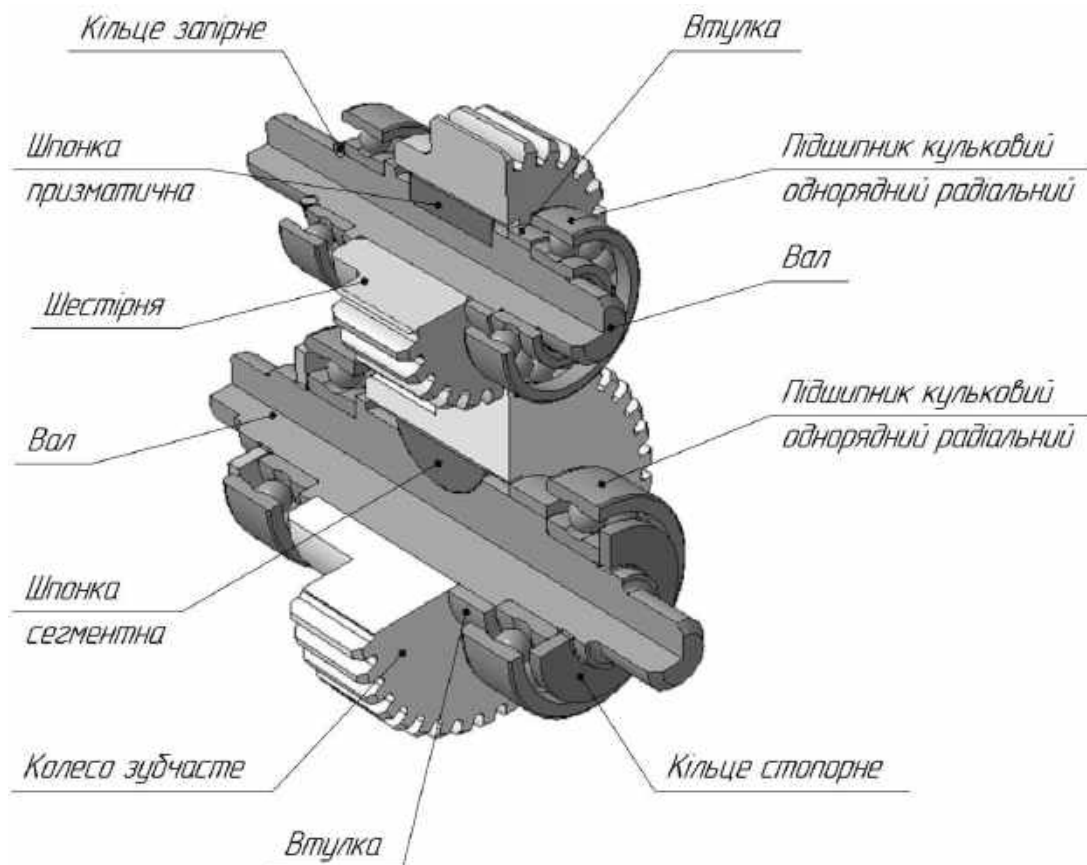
Деталі циліндричного зубчастого з'єднання з підшипниками
